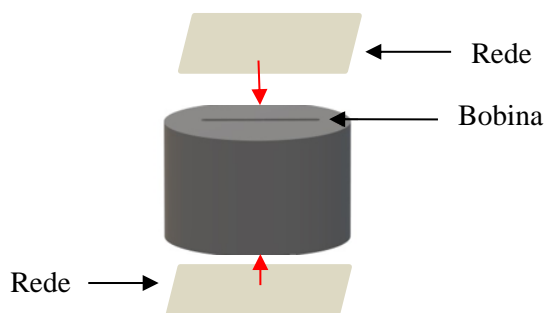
Esquema representativo da soldadura das redes à bobina.
